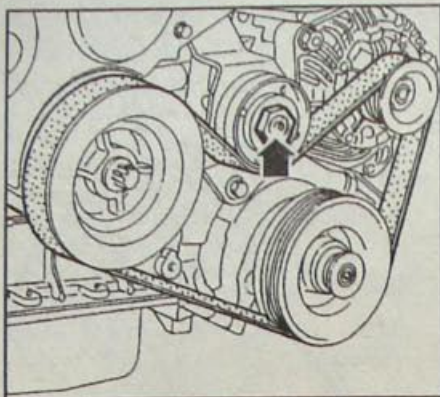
Расположение центрального болта крепления натяжного ролика ремня привода генератора
